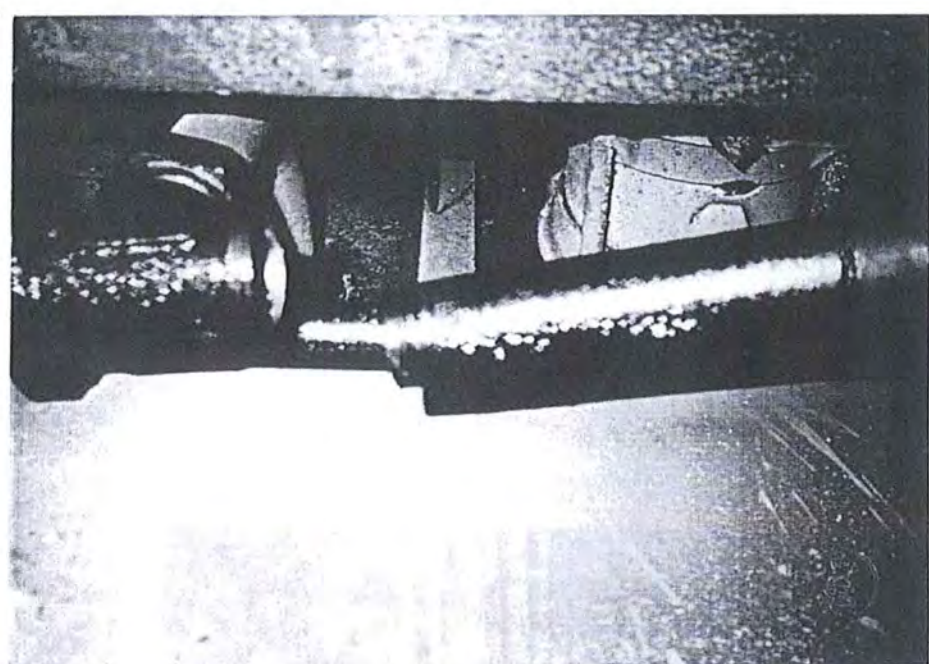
Retuolierøret med afgrening til betjeningspanel på bildæk. Røret trukket ud af skæringssamlingen til T-stykket.
